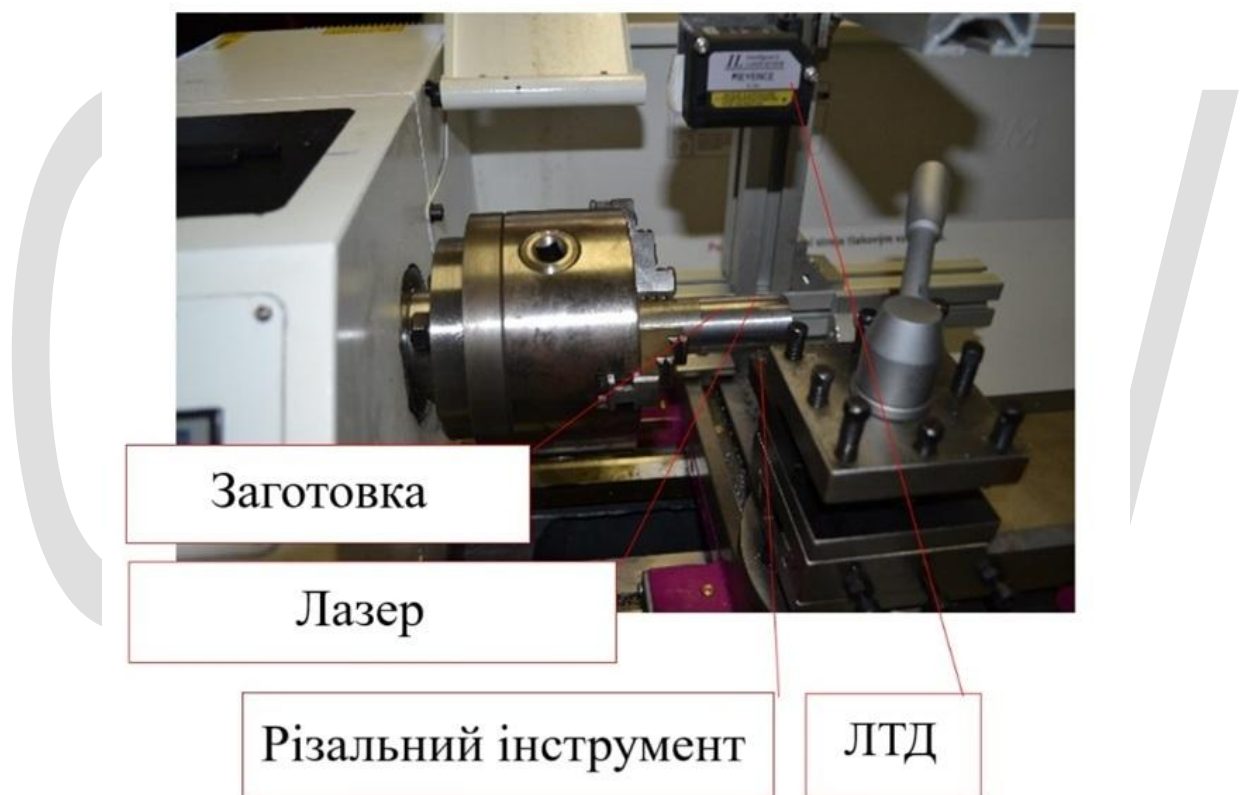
Загальний вигляд і робоча зона верстата Optimum TU 2807.
